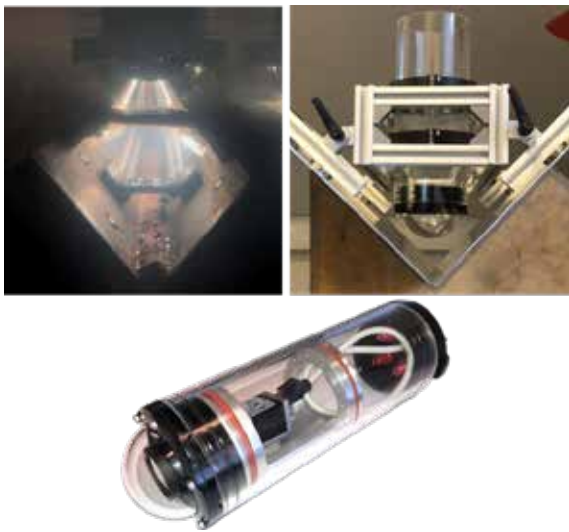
Links: Aufnahme einer Schweißnaht mit Referenzrahmen und objektfester Beleuchtung. Rechts: Führungsrahmen für den realen Einsatz an einer Kehlnaht (Seitenansicht). Unten: Verbaute Kamera im Unterwassergehäuse mit Dome Port
